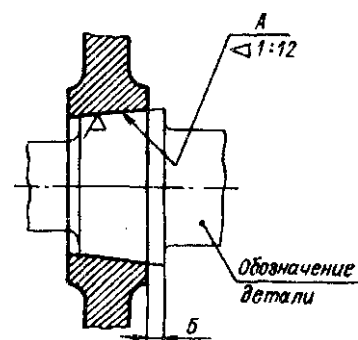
Чертеж детали, обрабатываемой по другой детали
